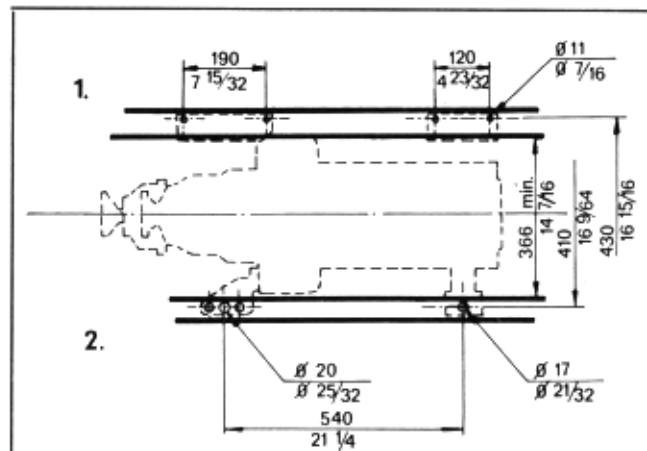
Motorbett 1 Gummiaufhängung 2 Feste Aufhängung
